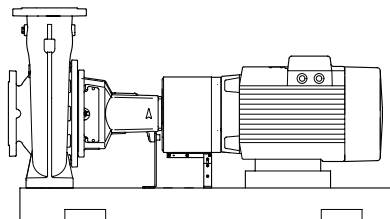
Vista esquemática de una bomba-motor NK montada en una bancada
